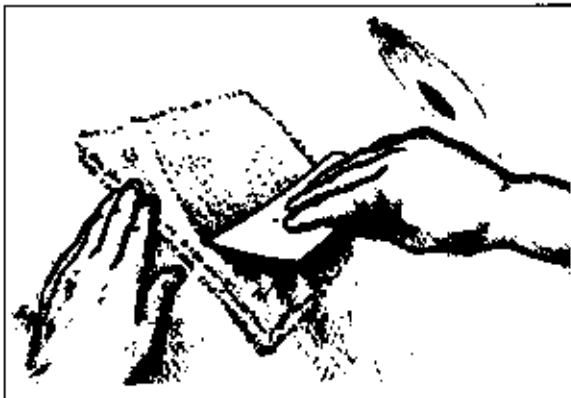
Streichen Sie das getränkte Laminat, das die Gegenplatte bilden soll, auf der gewachsenen Oberfläche glatt.
